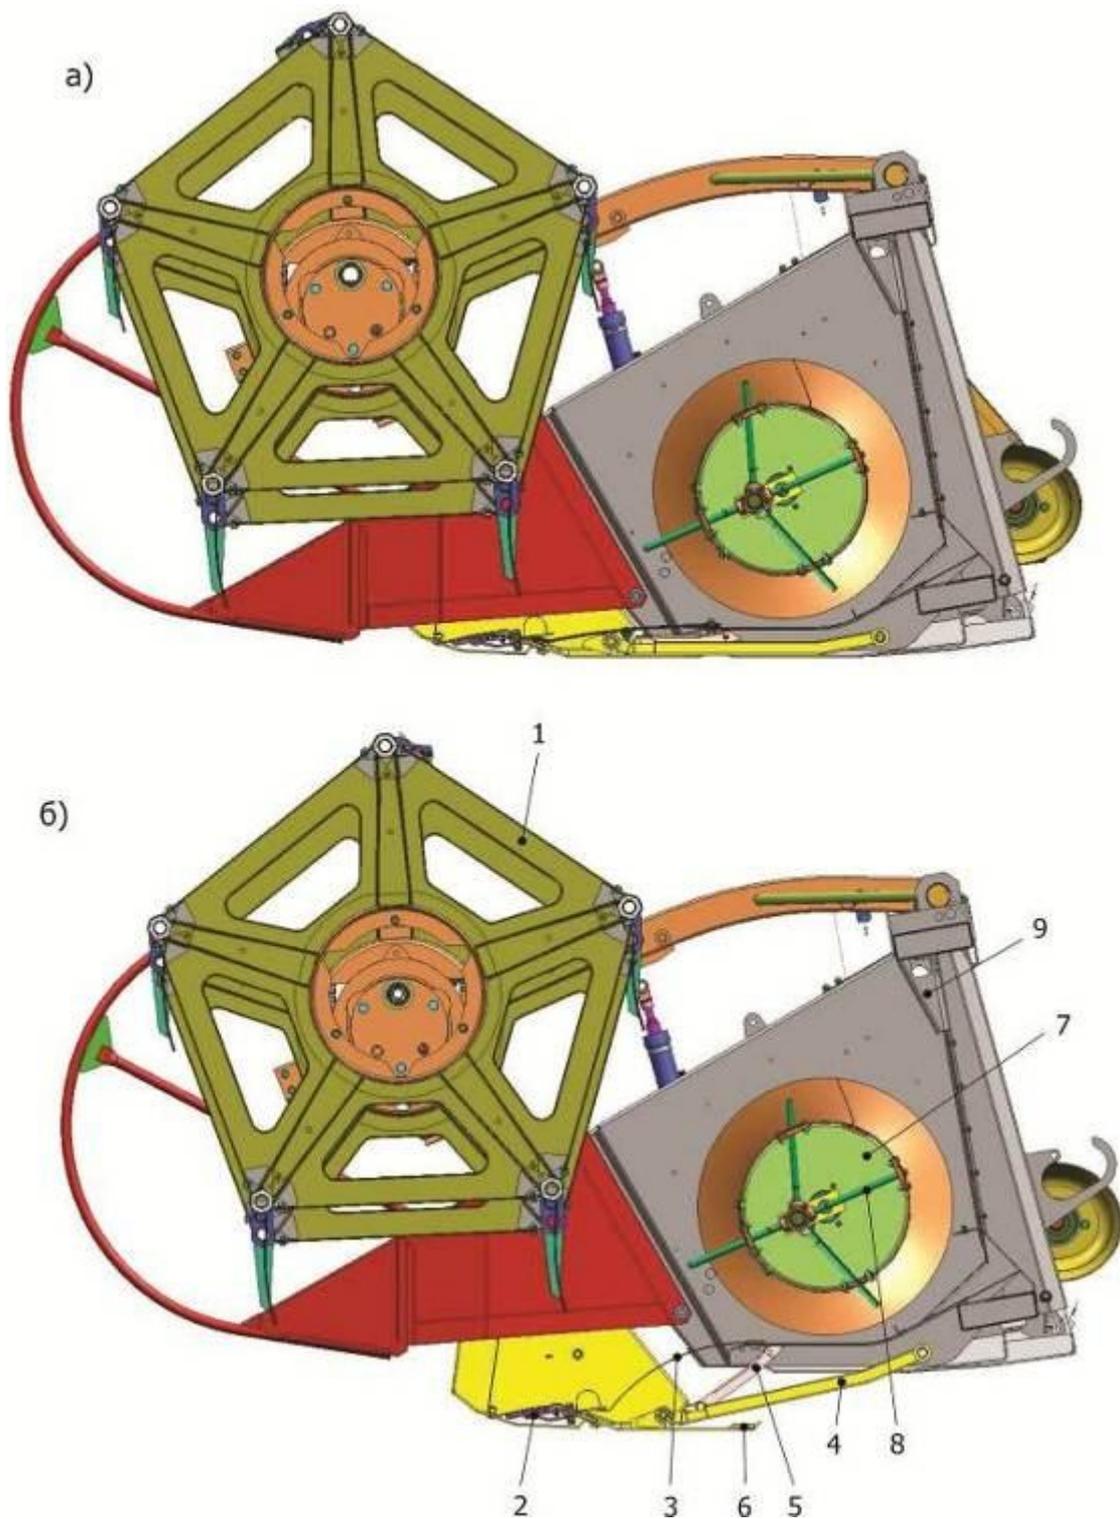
Схема работы жатки соевой универсальной ЖСУ-703 в режиме: а) "жесткий нож"; б) "плавающий нож"
